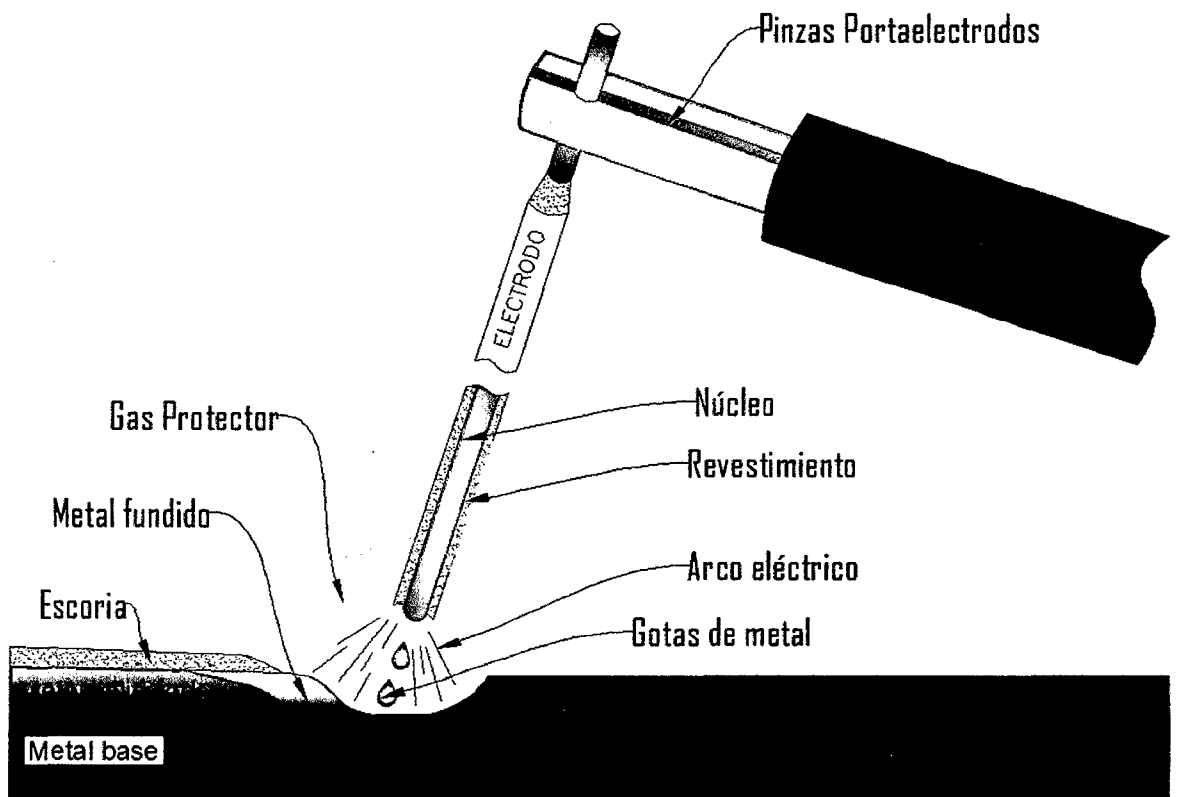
Esquema de Soldadura por Arco con Electrodo Revestido (SMAW)
